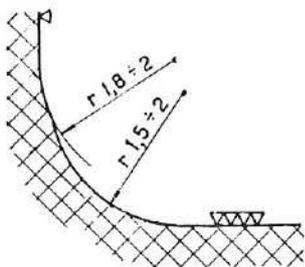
Chaflán para hacer sobre la muñequilla de apoyo. (Lado engranaje de la distribución).
